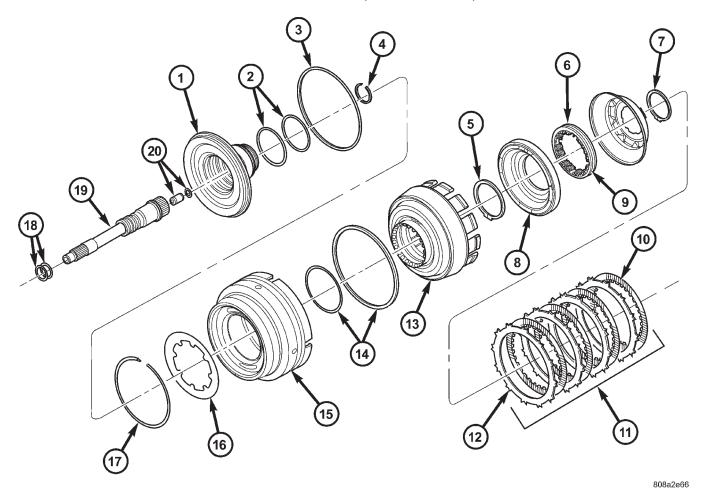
Conjunto de embrague de impulsión - Parte 1
